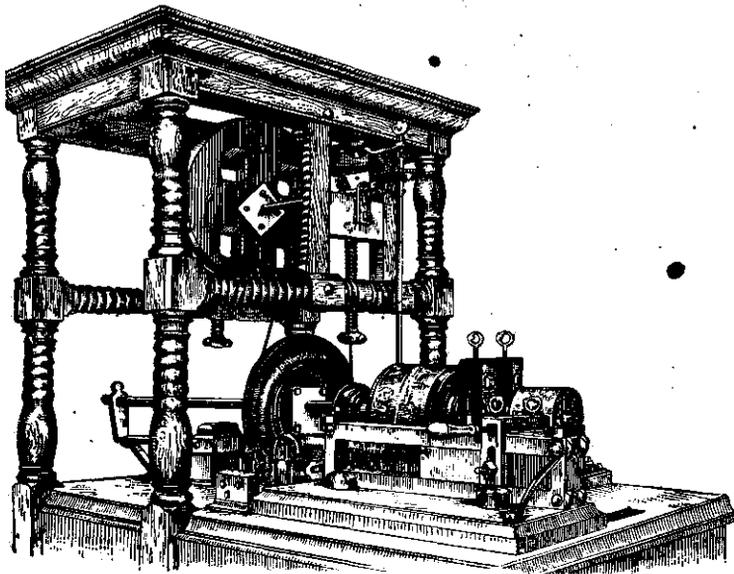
Токарно-копировальный станок 1712 г. (общий вид станка сзади).
